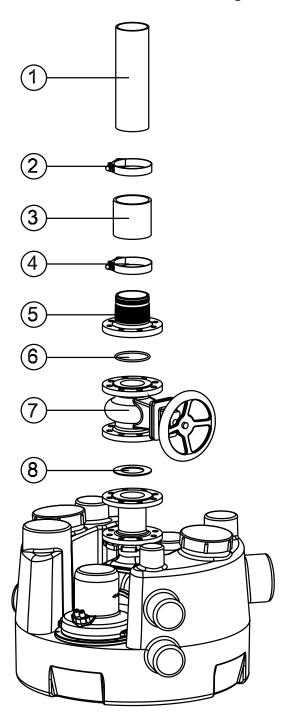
Installazione della valvola di arresto e del manicotto flangiato
